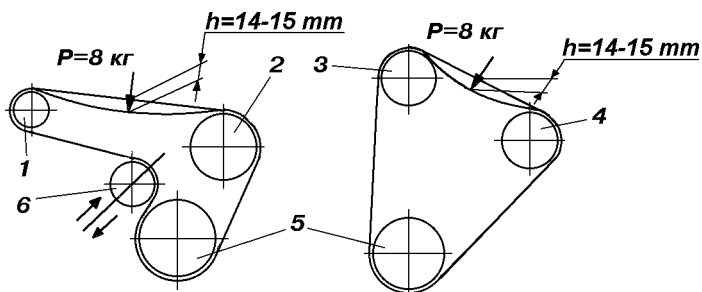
Схема натяжения ремня привода агрегатов:
